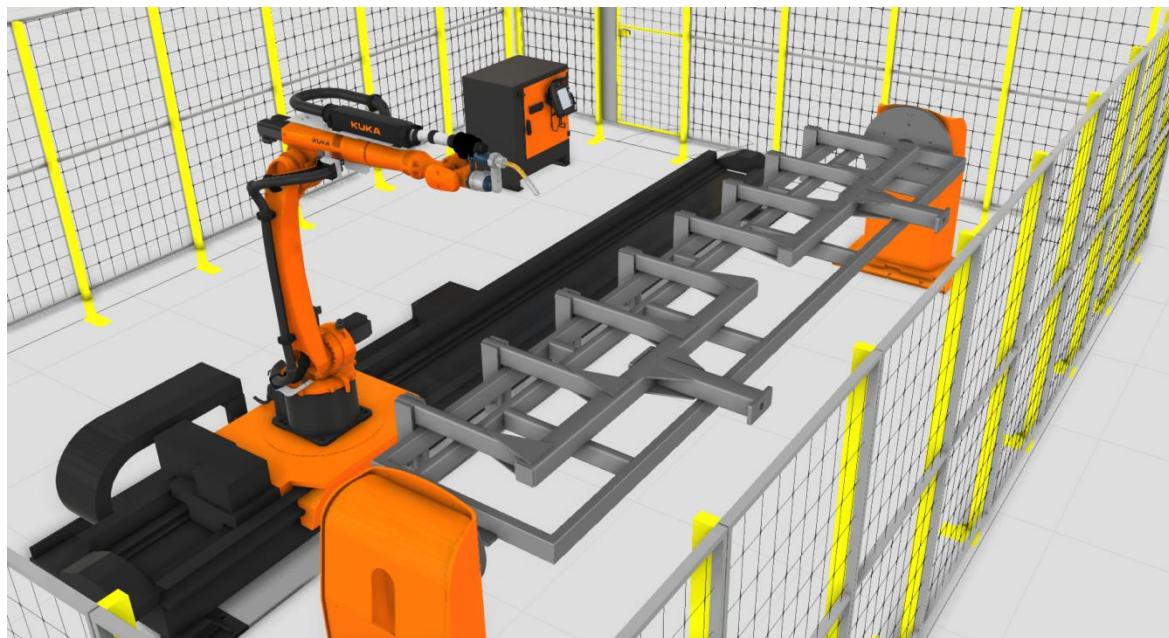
Общий вид цифрового двойника сварочного РТК
